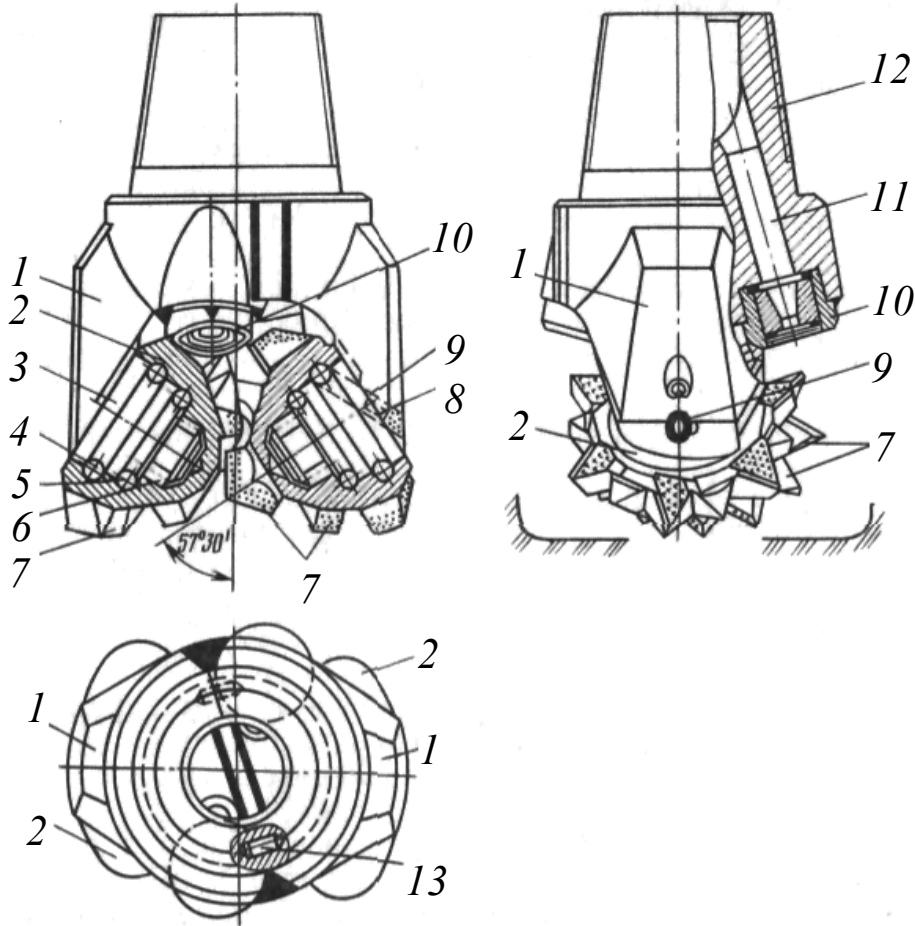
Конструктивные элементы долота для бурения в мягких породах с гидромониторными насадками: 1 – лапа; 2 – шарошка; 3 – цапфа; 4 – шариковый замковый подшипник; 5 – шариковый промежуточный подшипник; 6 – роликовый концевой подшипник; 7 – зубья шарошки, 8 – штифт-фиксатор; 9 – замковый палец; 10 – гидромониторная насадка; 11 – промывочный канал; 12 – присоединительная резьба; 13 – ориентирующий штифт
